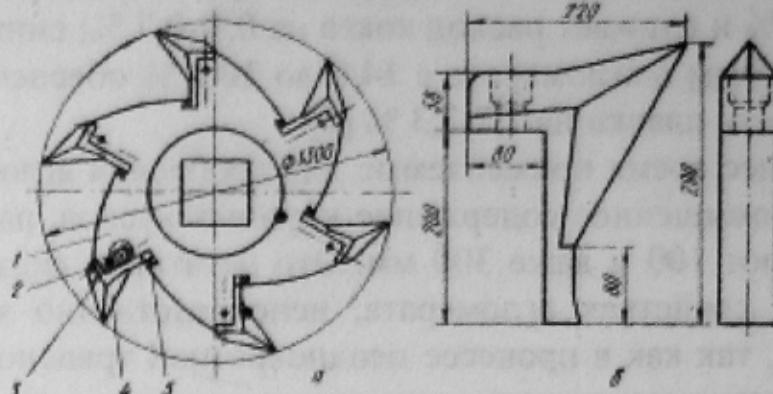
Звездочка одновалковой зубчатой дробилки: а – с самозатачивающимися зубьями; б – конструкция завода "Запорожсталь":
